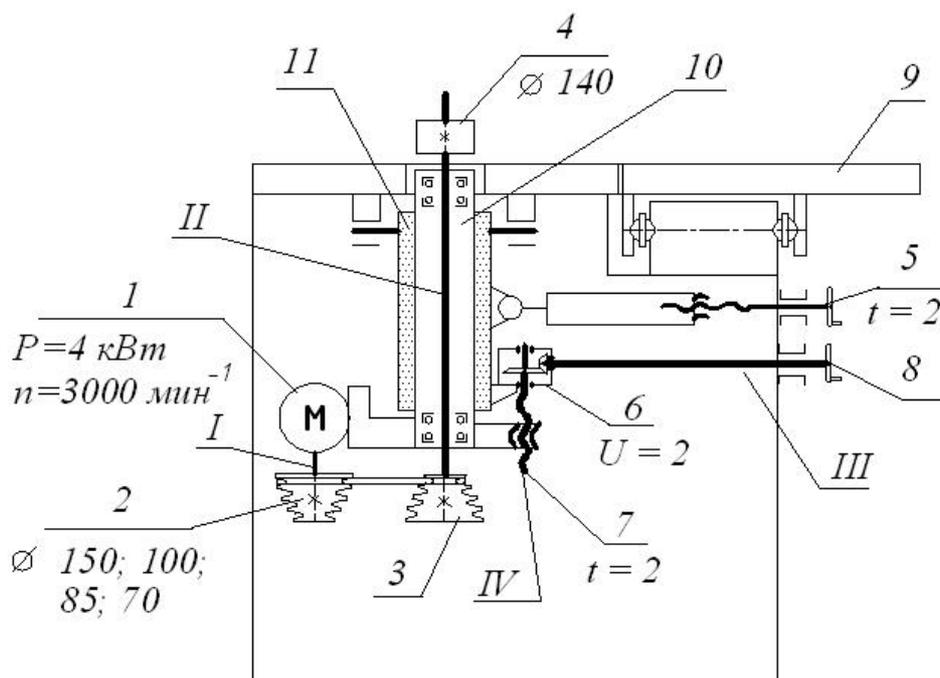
Фрезерный станок модели T1000 L с шипорезной кареткой
